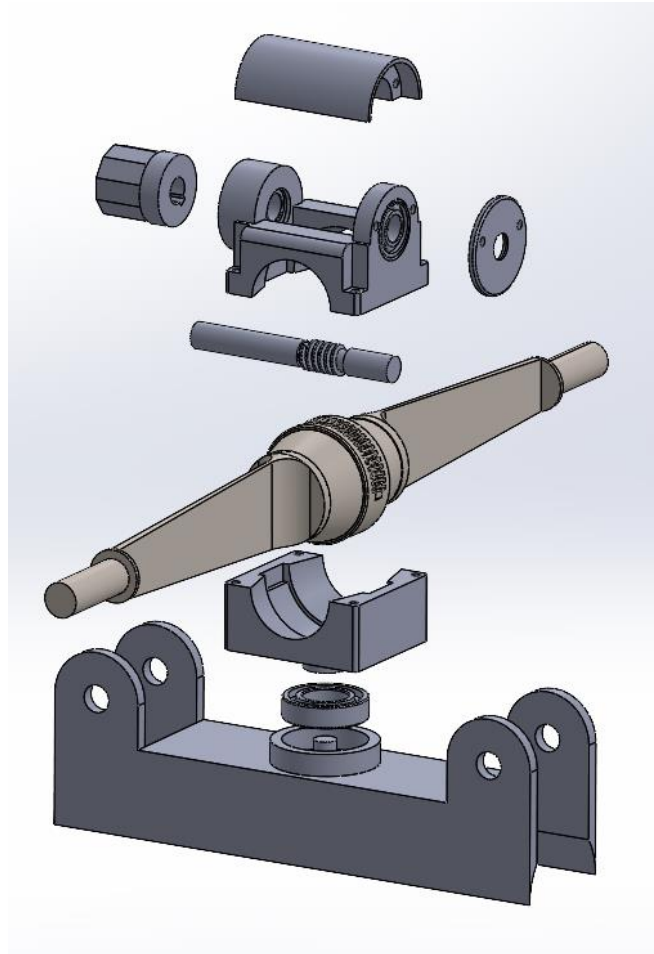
Vista explosionada del diseño de la barra estabilizadora de rigidez regulable mediante giro de las placas
